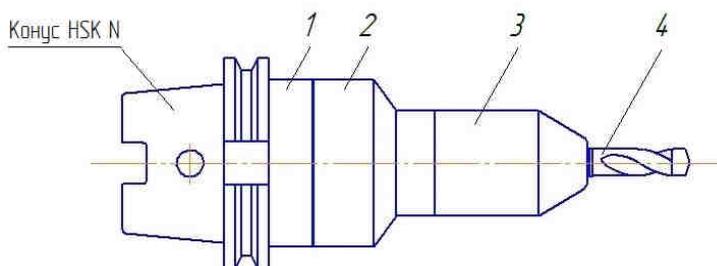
Инструментальная наладка для осевых режущих инструментов с используемыми модулями: 1 – базовым;
